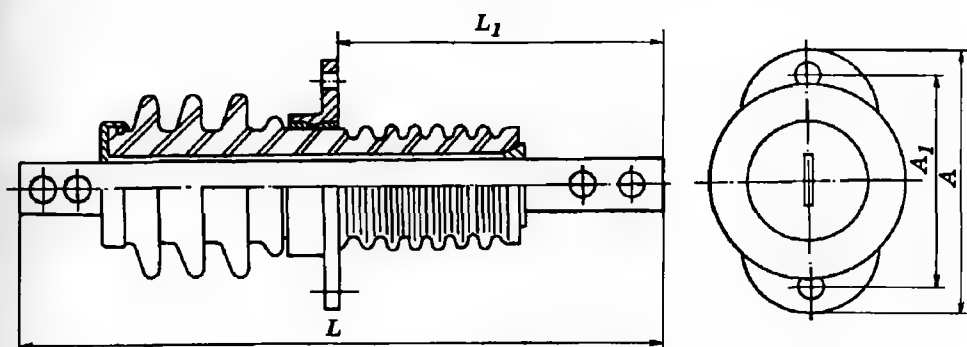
Проходной изолятор для наружно-внутренней установки категории Б
